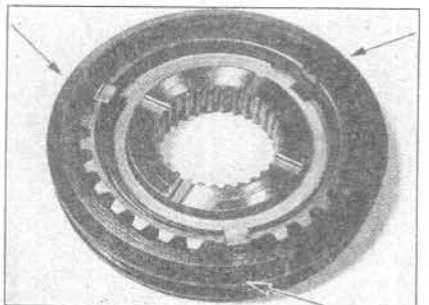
Направление установки распорных пружин синхронизатора (Глава 9)
